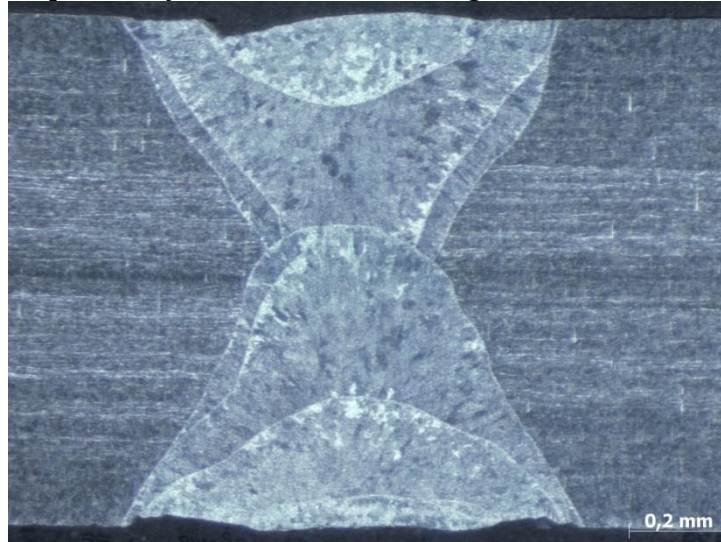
Macroscopia da seção transversal da soldagem com 70% de sobreposição.
